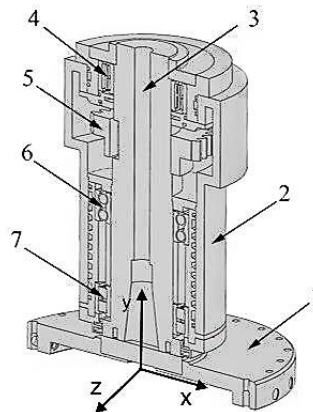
3D модель шпиндельного вузла у розрізі: 1 – торцева фреза; 2 – корпус; 3 – шпиндель; 4 – дворядний роликовий радіальний підшипник; 5 – зубчасте колесо; 6 – радіально-упорний кульковий дворядний підшипник; 7 – дворядний роликовий радіальний підшипник
